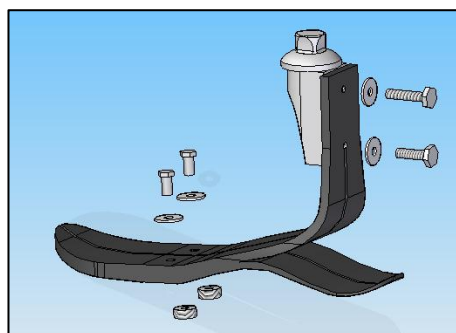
Vista explosionada del tubo con los encajes. Solid Edge.
